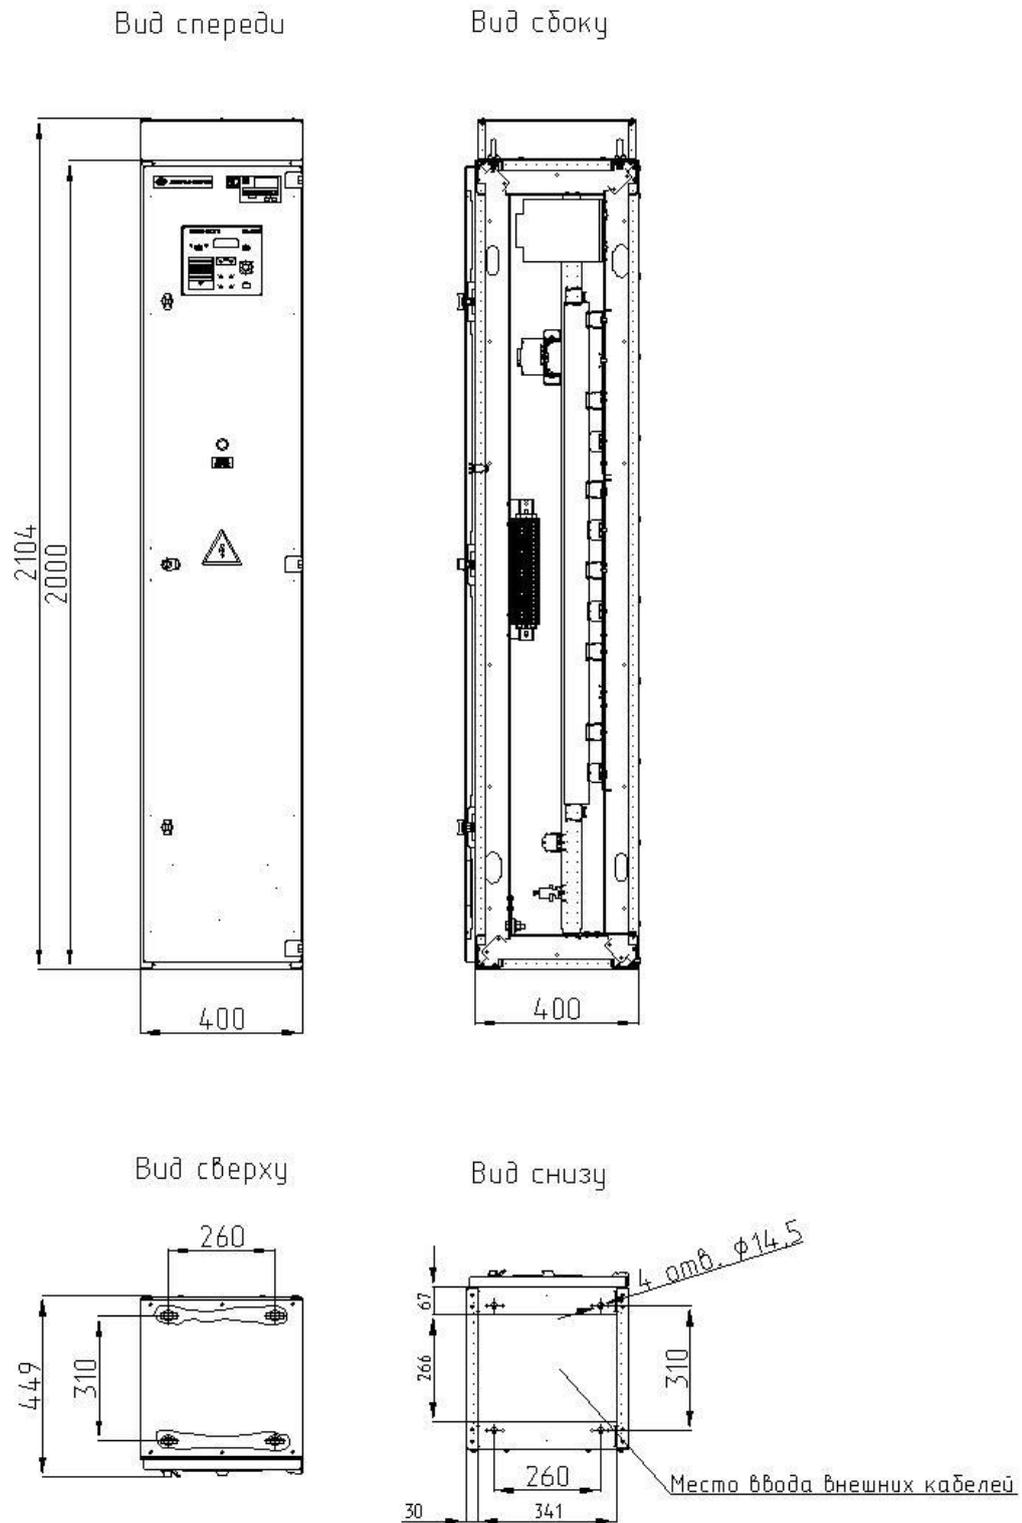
Габаритный чертеж шкафа управления и защит
